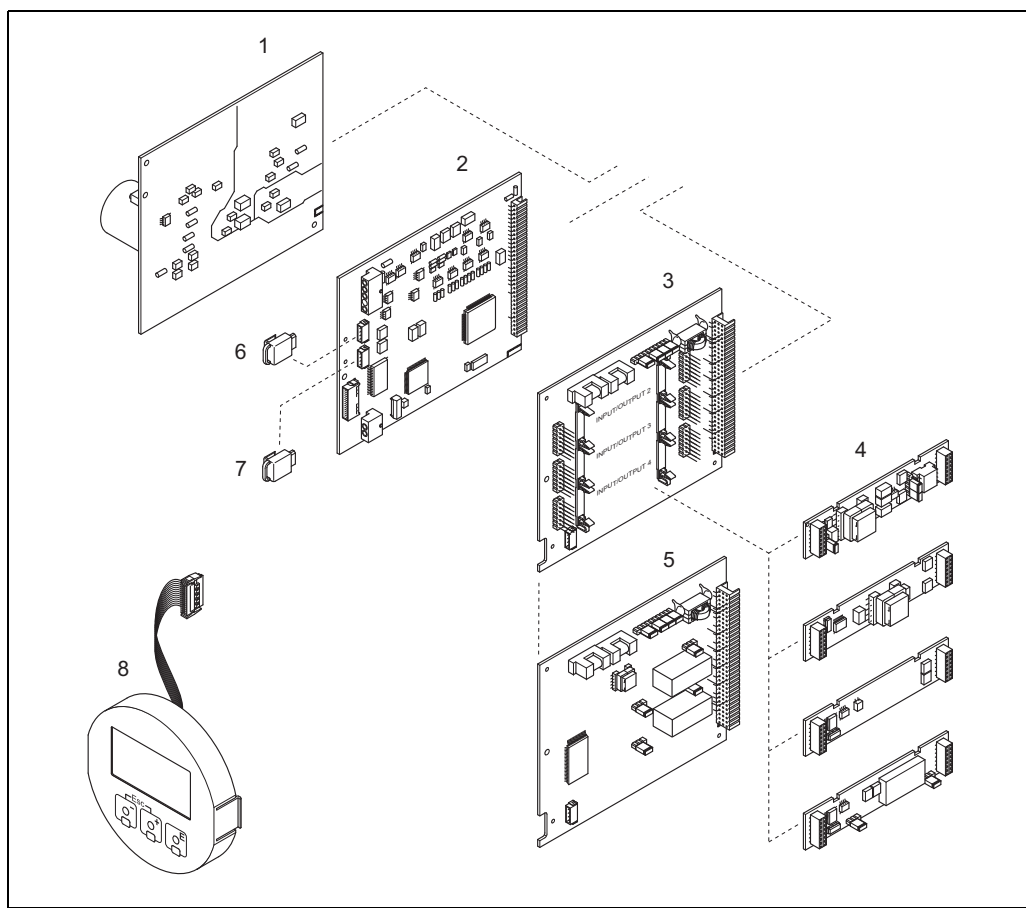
Запасные части для преобразователя 84 (погружной корпус и корпус с настенным монтажом)
